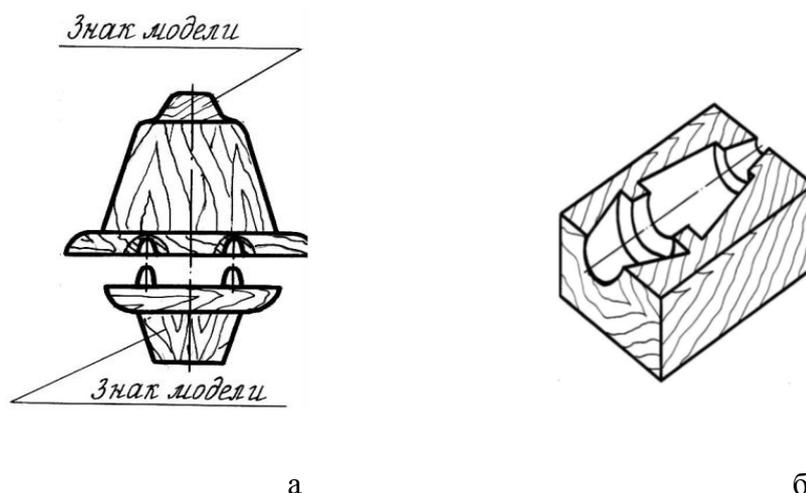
Модель отливки (а) и половинка стержневого ящика (б)
